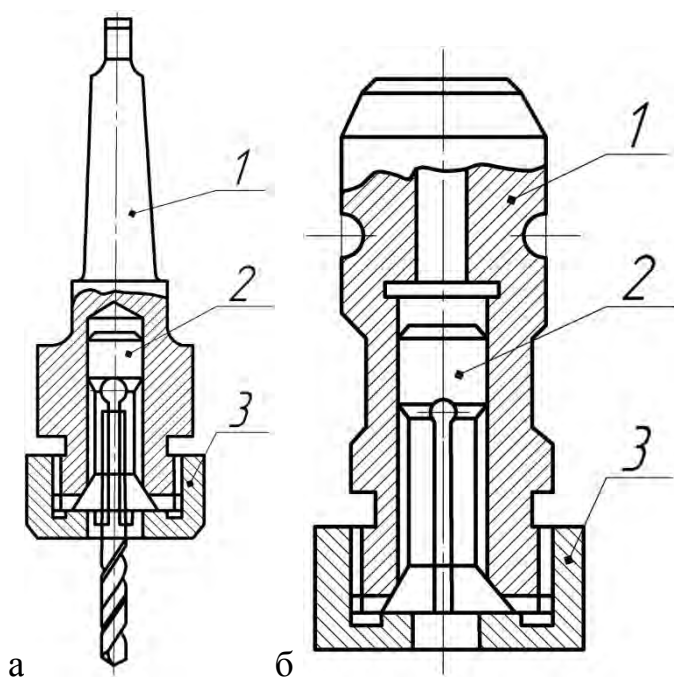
Цанговые сверлильный патрон (а) и вставка (б)
